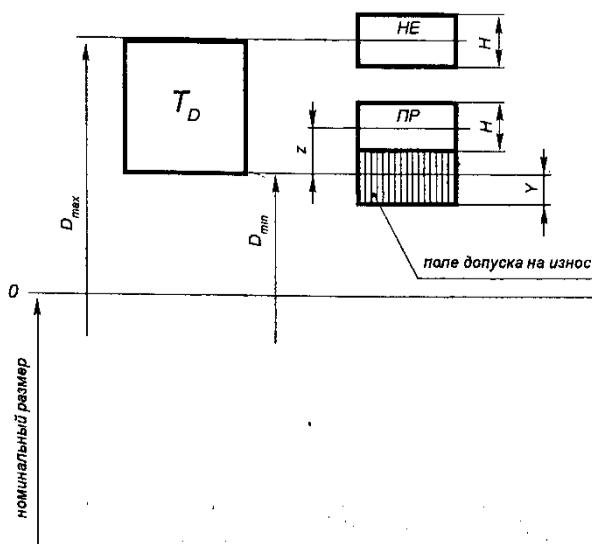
Схема расположения полей допусков калибров для контроля отверстий изготовленных по квалитетам 6, 7 и 8 при номинальных размерах до 180 мм (для размеров отверстий изготовленных по квалитетам от 9 до 17, $Y = 0$)
